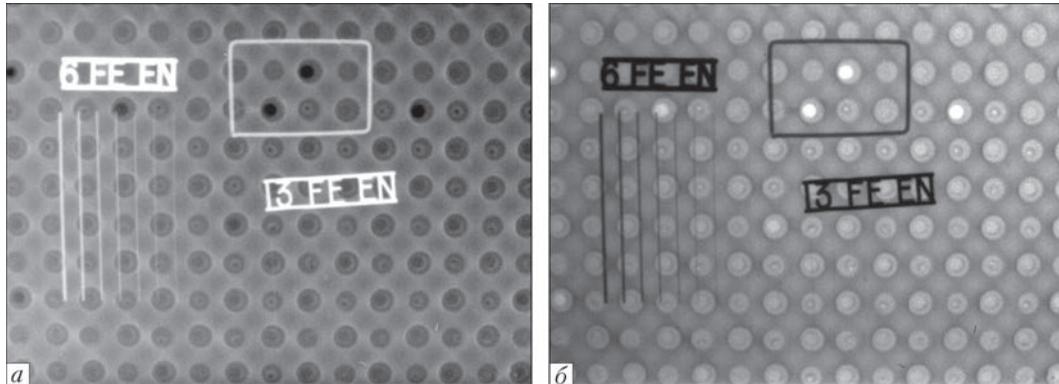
Цифровые изображения образца с двойной точечной сваркой с локализацией участка для исследования с помощью твердотельного преобразователя S10811-11: *а* – негатив; *б* – позитив
